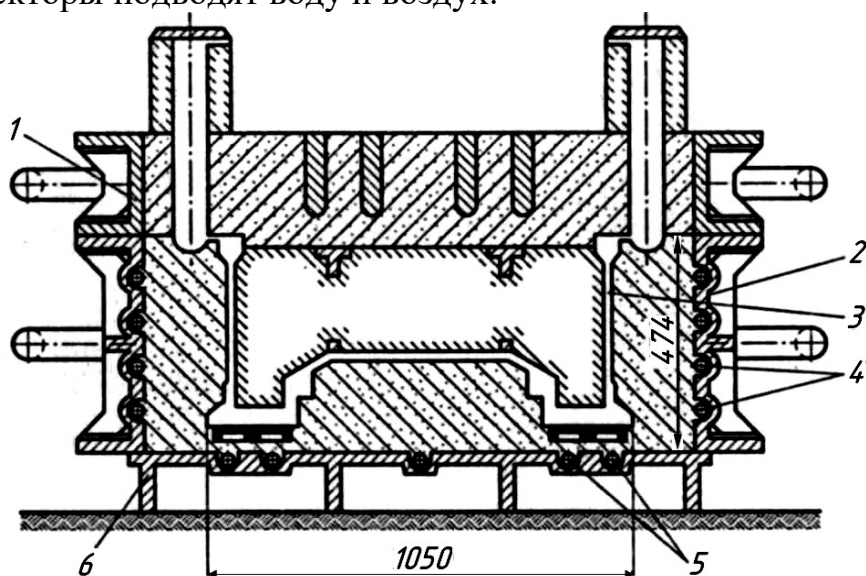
Конструкция оснастки для охлаждения отливок: 1 – верхняя полуформа; 2 – нижняя полуформа; 3 – отливка; 4 – боковая система труб с отверстиями; 5 – то же, нижняя; 6 – постельная плита
